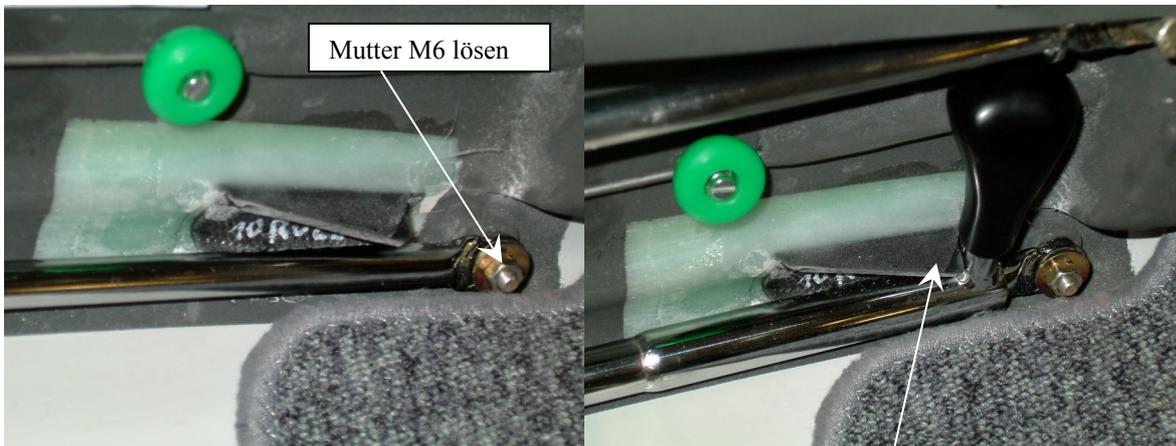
& 3: betroffener Bereich am Fahrwerkshebel
